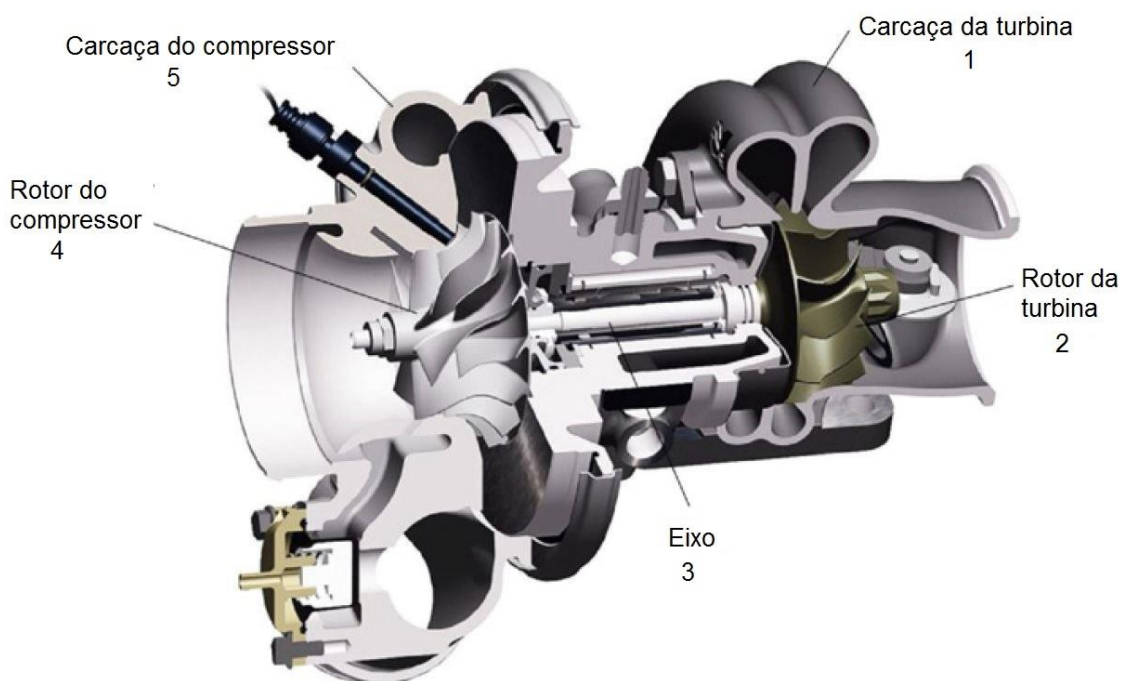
Turbocompressor em corte transversal – principais componentes
